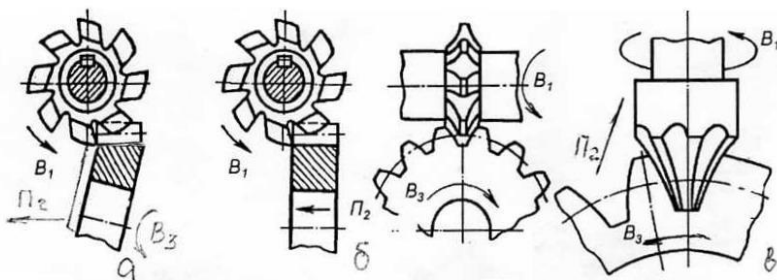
Схемы обработки зубьев зубчатых колес модульными фрезами методом копирования – касания:
